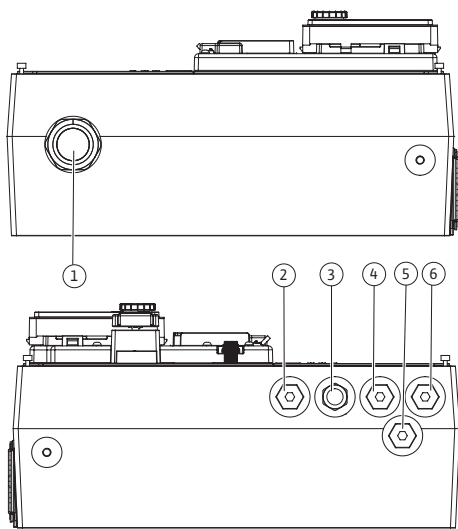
Kabelverschraubungen/Kabeldurchführungen (11 kW ... 22 kW)
